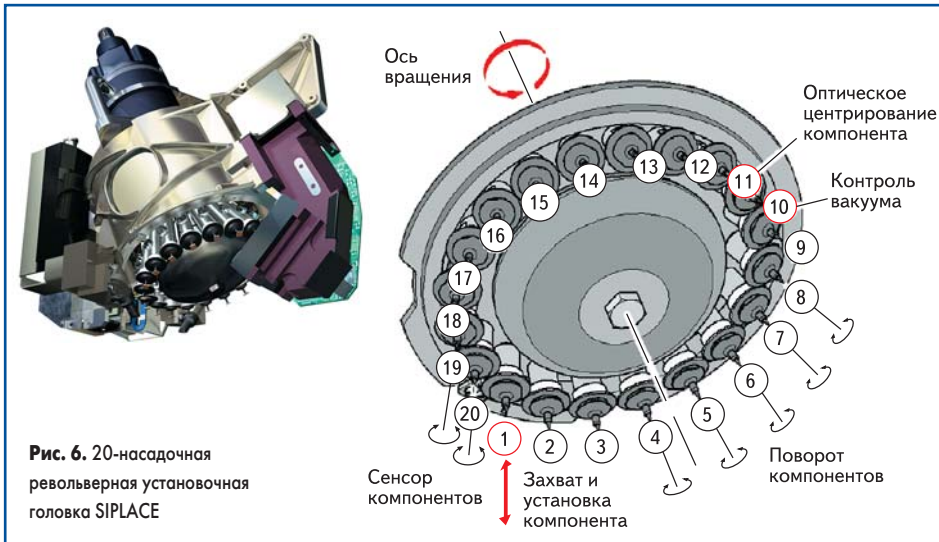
20-насадочная револьверная установочная головка SIPLACE
